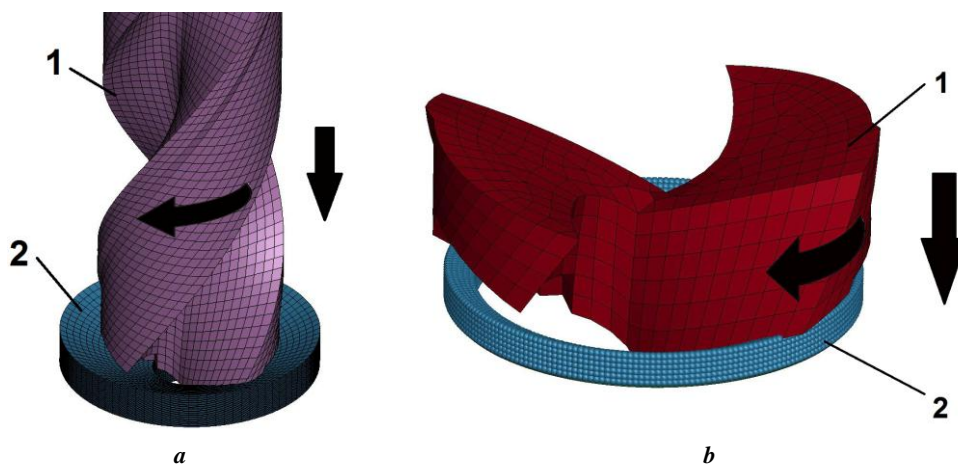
Схема процесса сверления цилиндрической заготовки методом Лагранжа (а) и трубной заготовки методом Галеркина (б): 1 – сверло, 2 – заготовка
